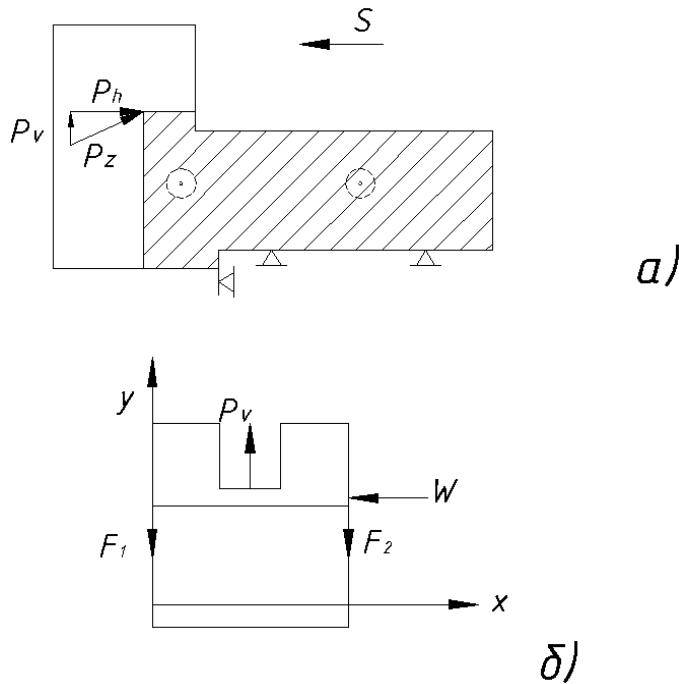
Схеми для розрахунку зусилля кріплення заготовки
